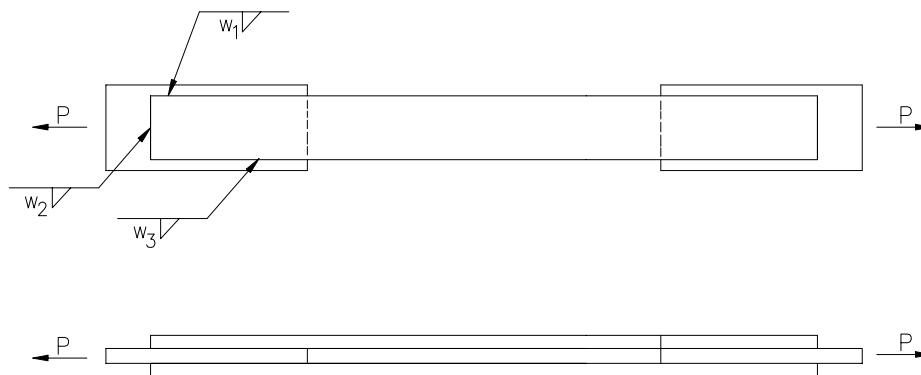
Configuração das amostras de chapas soldadas para testes
